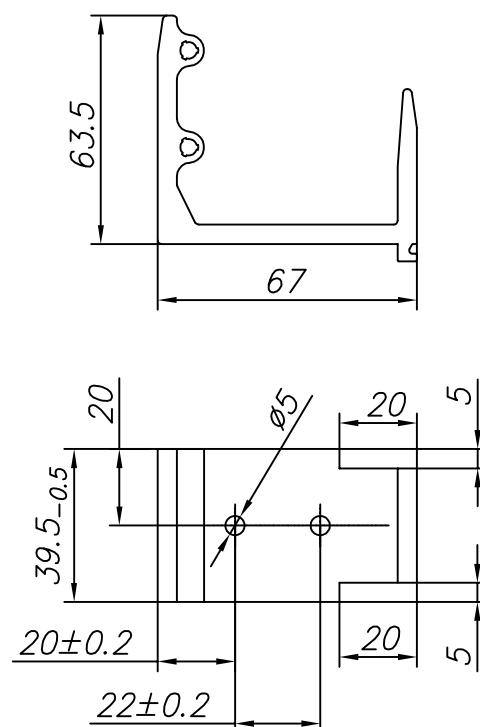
Изготовление соединителя FLGU.400.0912
